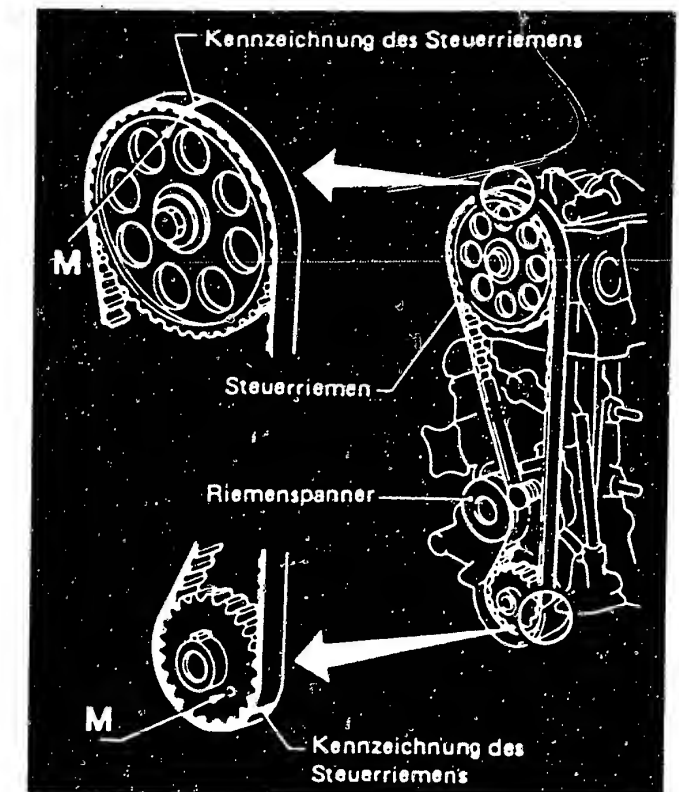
Kennzeichen (M), die beim Einbau des Zahnriemens zu beachten sind.
